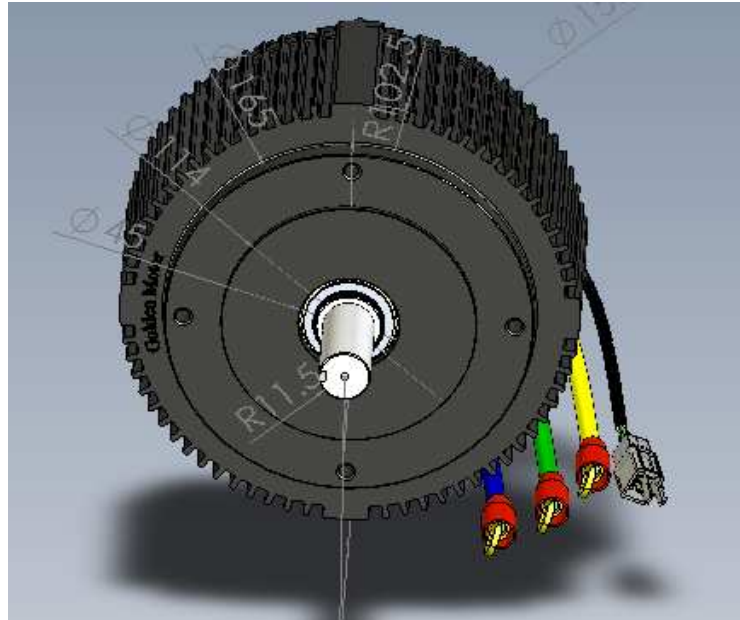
Motor Golden Motor HPM-5000L – Cables de conexión.
